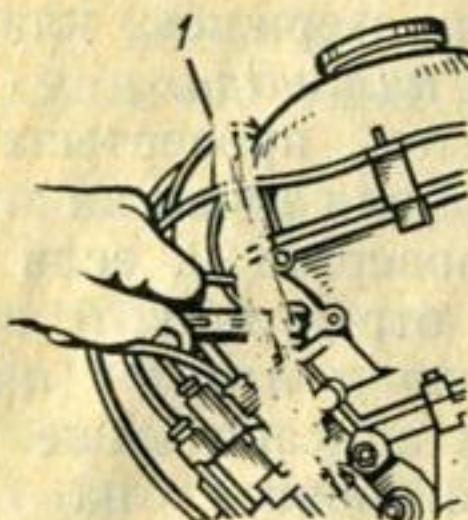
Регулировка натяжения цепи привода газораспределения:
